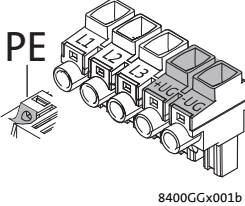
Entfernen der Kontaktschrauben bei Gerätegröße 4 ... 6 (netzseitig und motorseitig)
